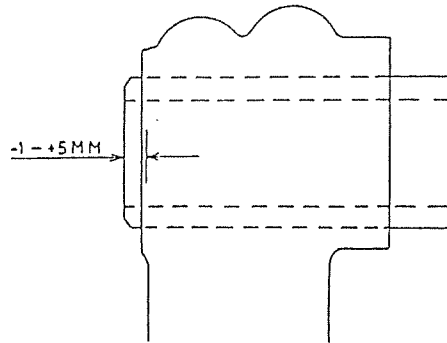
Axelns läge i förhållande till fjäderarmen. Bakre fjädring.
